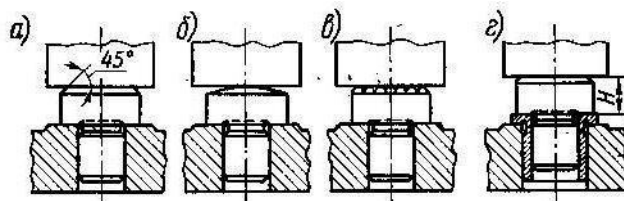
Опорные штыри (а – с плоской головкой; б – со сферической головкой; в – с насечённой головкой; г – установка штырей в стальные закалённые переходные втулки, запрессованные в отверстия корпуса; H – размер, выдерживаемый при изготовлении штырей)
